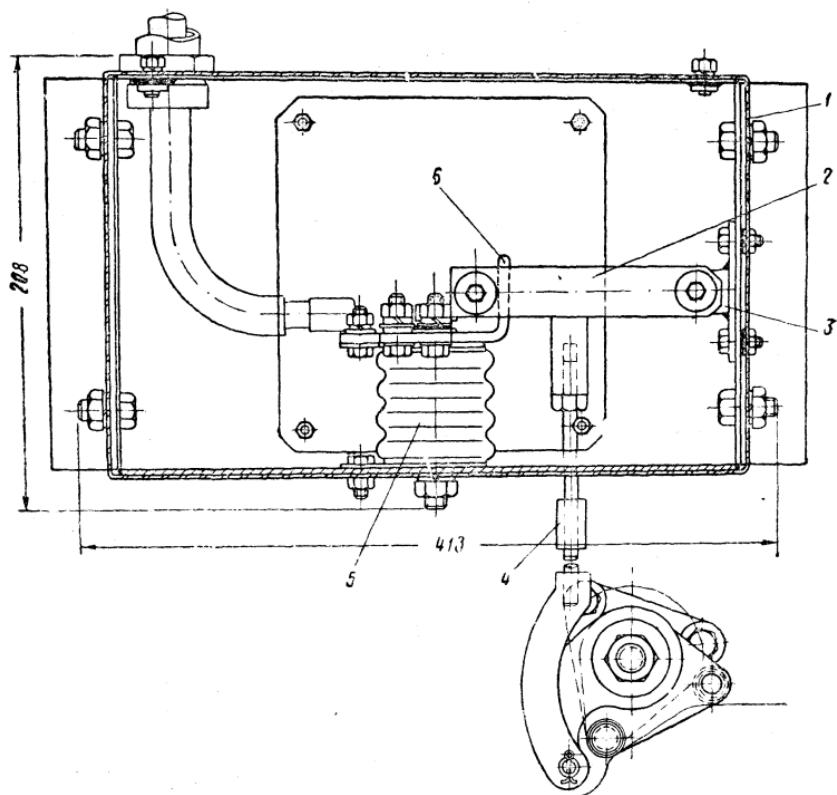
Разъединитель высоковольтный однополюсный КЗ-1:
